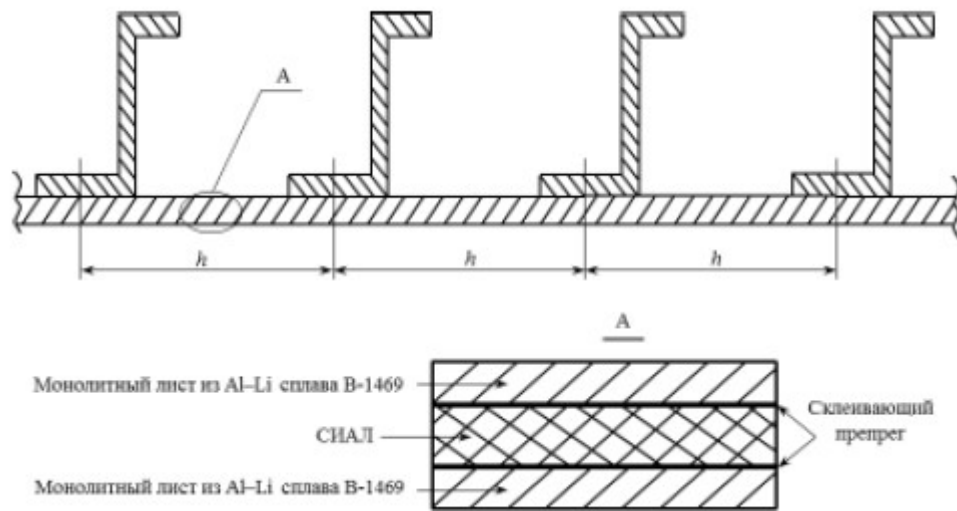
Конструктивно-подобный образец с гибридной обшивкой
